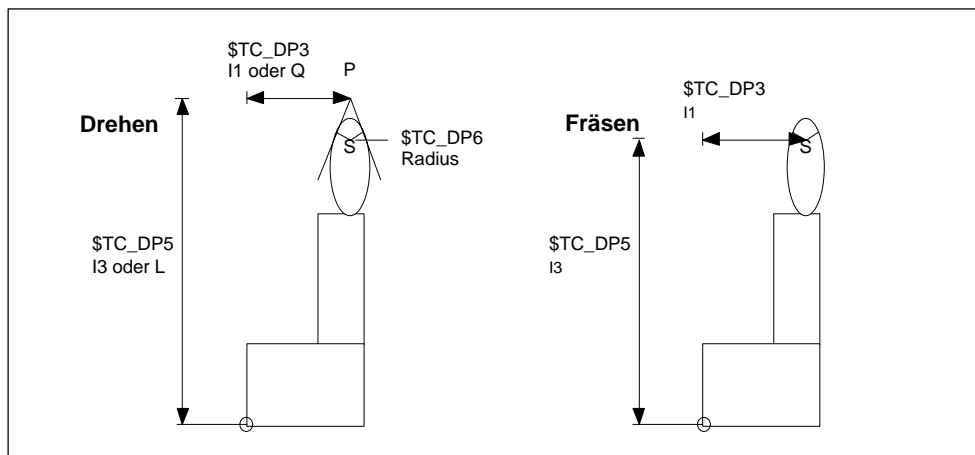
Dreh- und Fräs-Werkzeuge – Zusammenhang Schneidenlage und Radiuskorrektur
